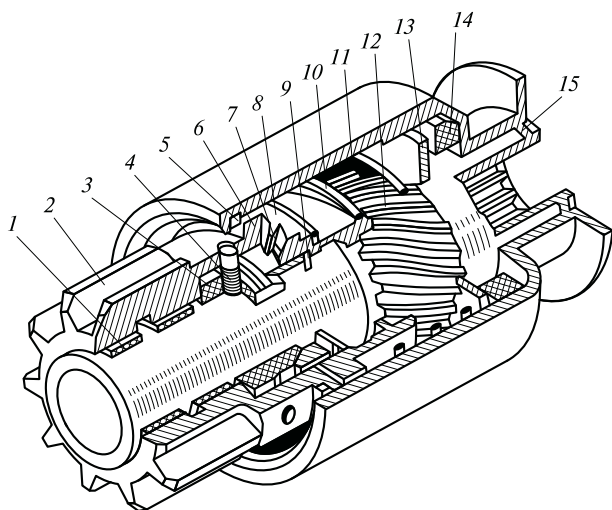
Приводной механизм с храповичной муфтой свободного хода: 1 — вкладыш; 2 — шестерня; 3 — сегмент (сухарик); 4 — направляющий штифт; 5 — замковые кольца; 6 — ведомый храповик; 7 — коническая втулка; 8 — ведущий храповик; 9, 13 — шайбы; 10 — пружина; 11 — корпус муфты; 12 — шлицевая направляющая втулка; 14 — буферное резиновое кольцо; 15 — поводковая муфта
